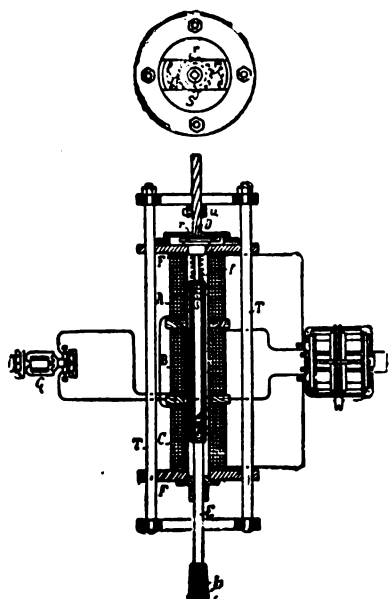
e 2. — Perforatrice a solenoidi di Werner Siemens. — Schema.
